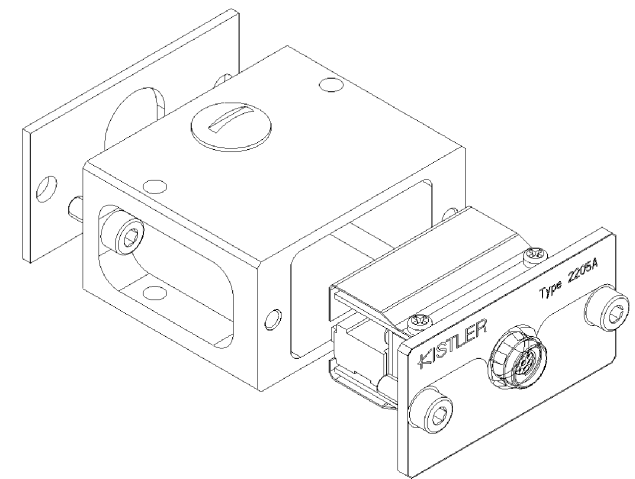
Einbau in Gehäuse für Montage am Spritzgießwerkzeug
